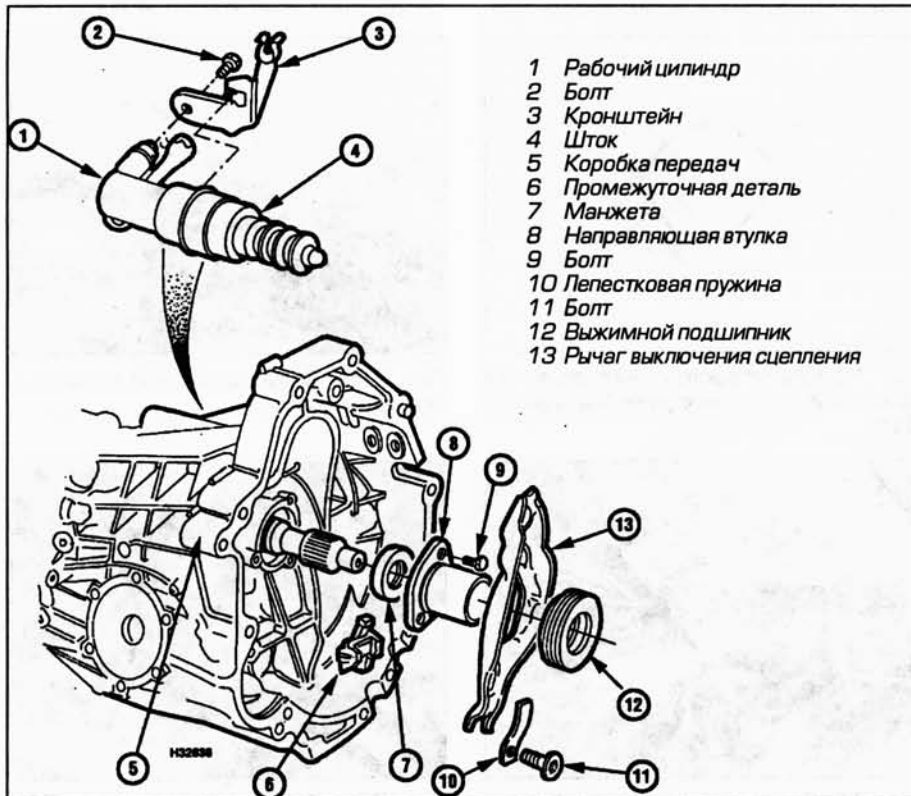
,г. Механизм выключения сцепления (коробки передач 01E)
